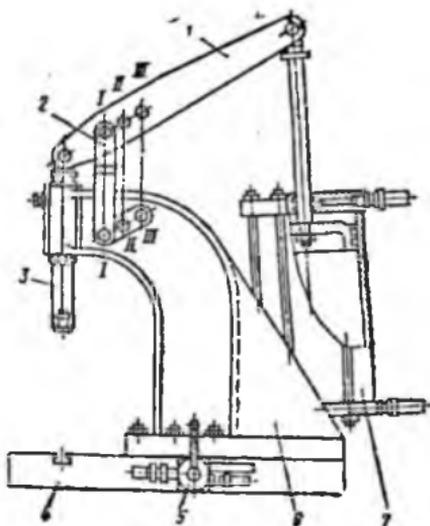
Пневморычажный пресс конструкции ВПТИСТРОЙДОРМАШ:
